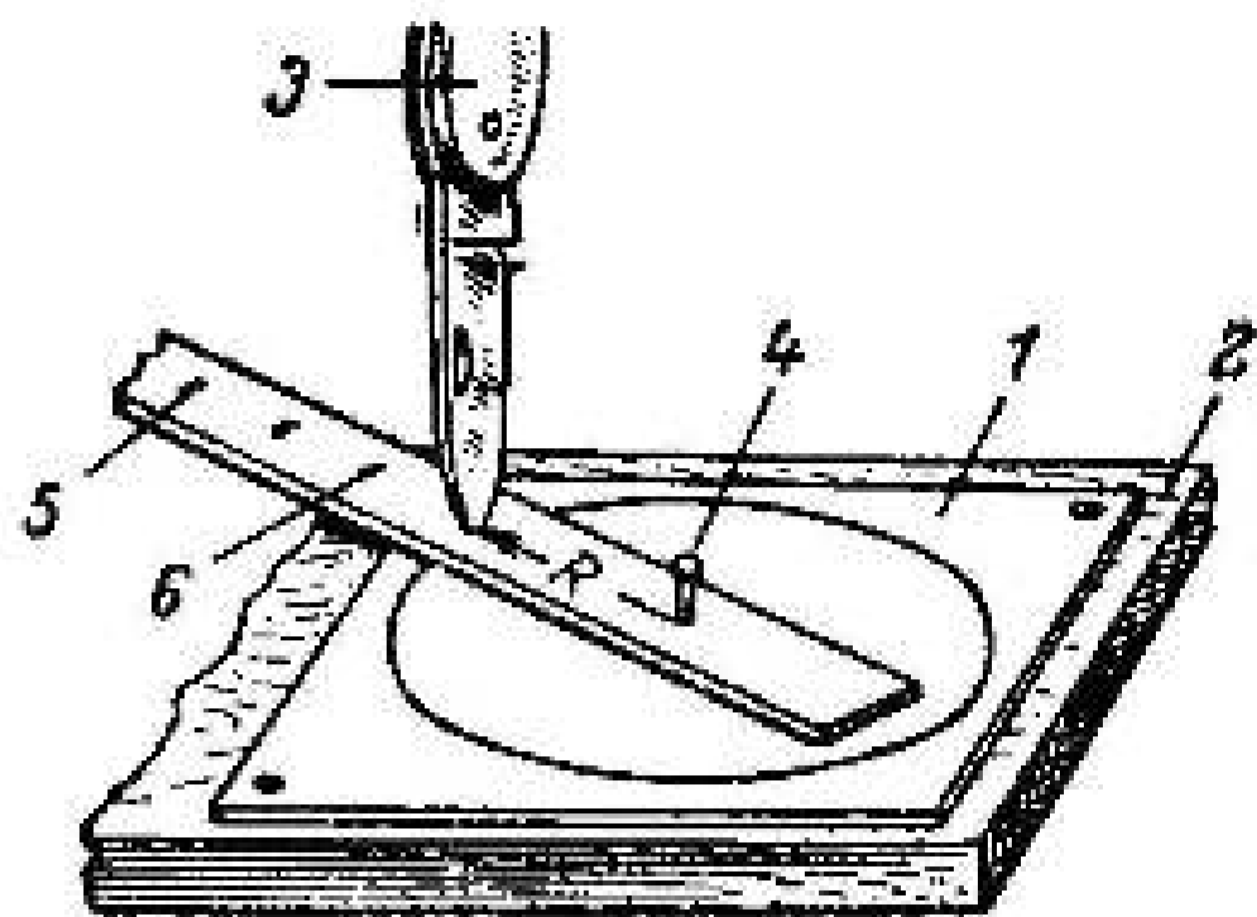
Приспособление для вырезки кружков и колец: 1 — фанера; 2 — доска; 3 — нож; 4 — гвоздь; 5 — планка; 6 — вырезы в планке
